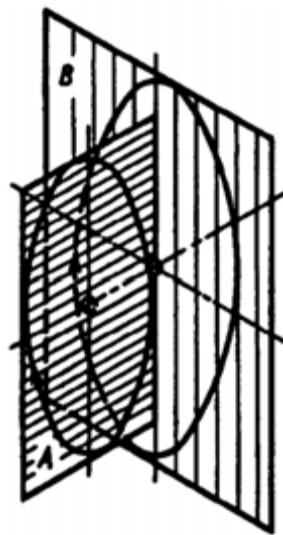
Схема фрезерування тіл обертання торцевими фрезами
